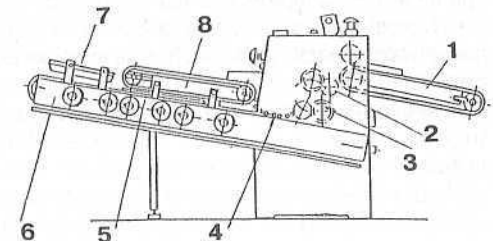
Тістозакатна машина Т1-ХТ2-3: 1 — подаючий транспортер, 2, 3 — розкочуючі валки, 4 — завиваюча решітка, 5 — бокові направляючі для зарівнювання кінців тістових заготовок, 6 — несучий транспортер, 7 — формуюча плита, 8 — закрючуючий транспортер
